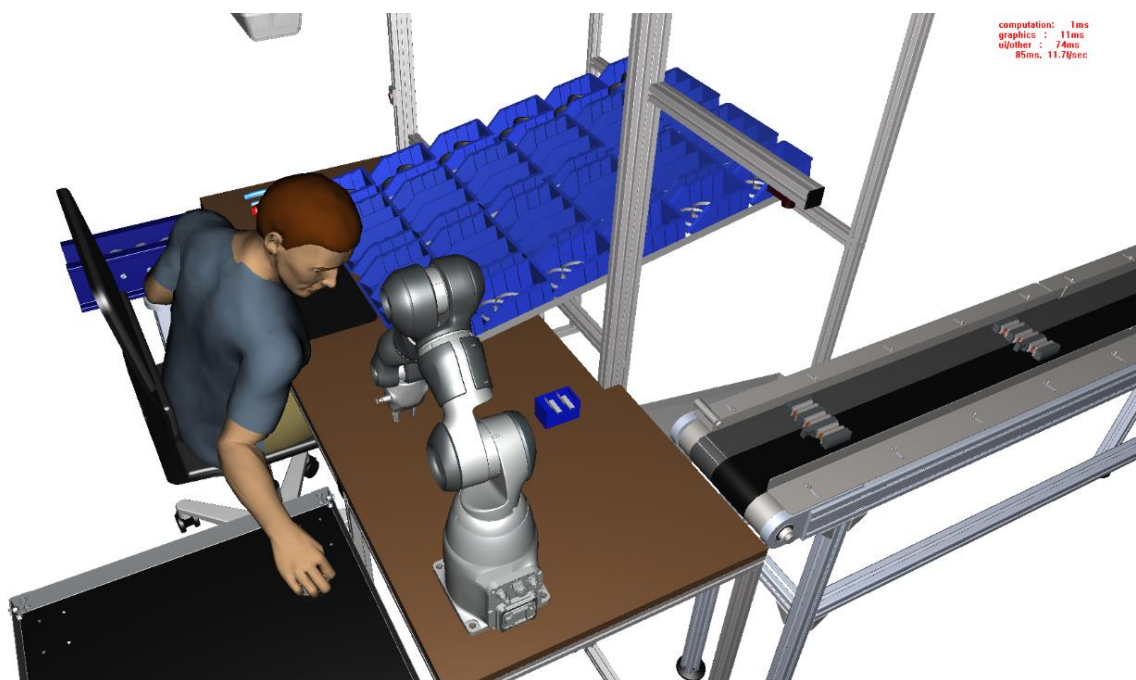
Operace 390: Vyjmutí statoru z přípravku
